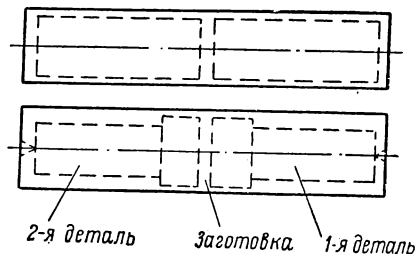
Пример изготовления двух деталей из одной заготовки.
